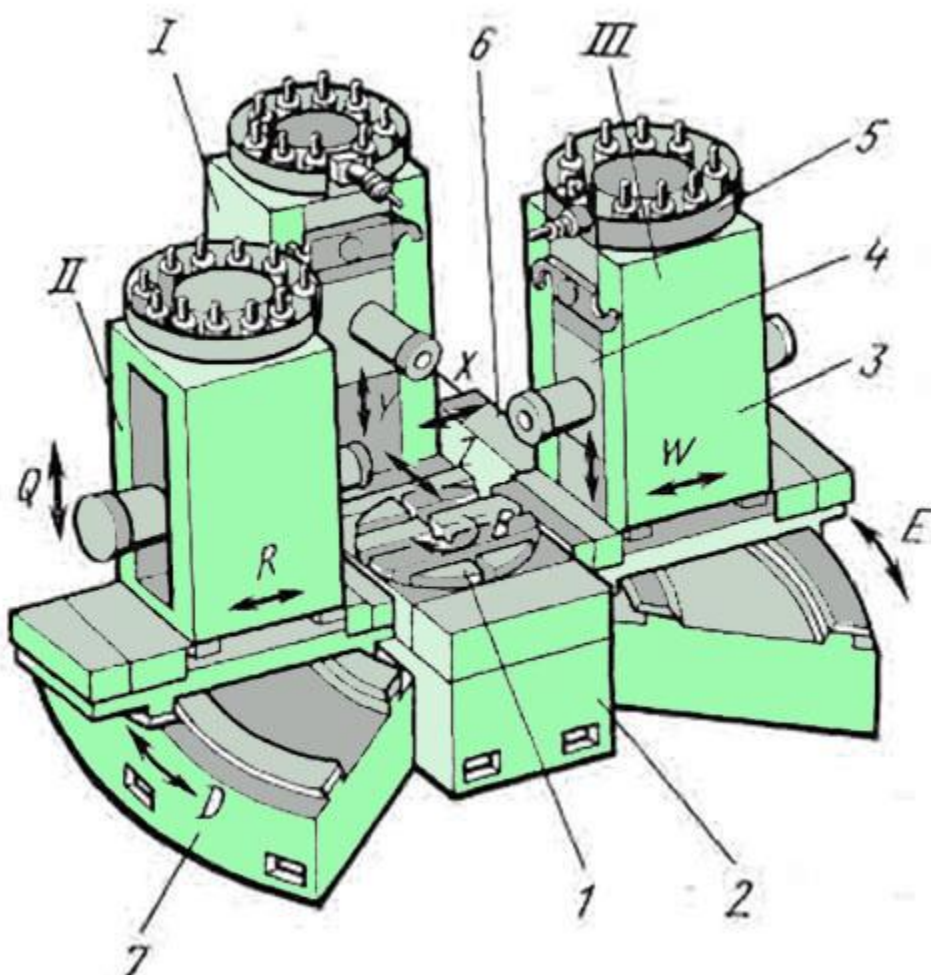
Компоновка агрегатного станка с ЧПУ
